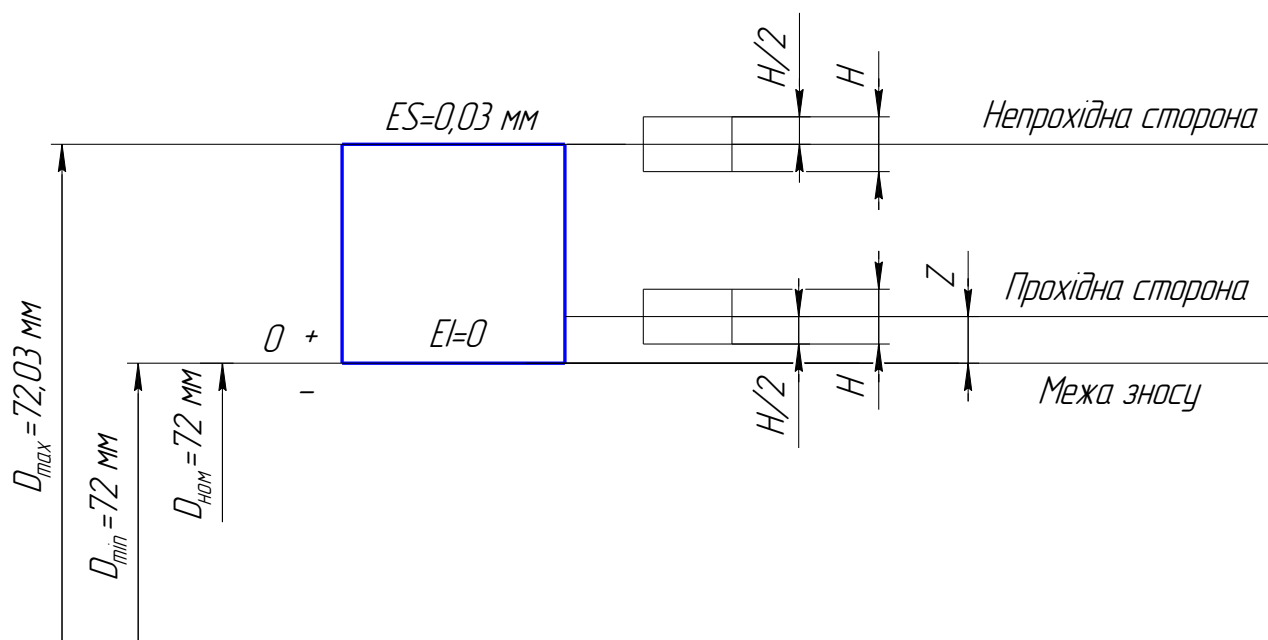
Схема розташування допусків робочих поверхонь калібрів для контролю розміра  $\text{Ø}72\text{H}7(^{+0,03})$
